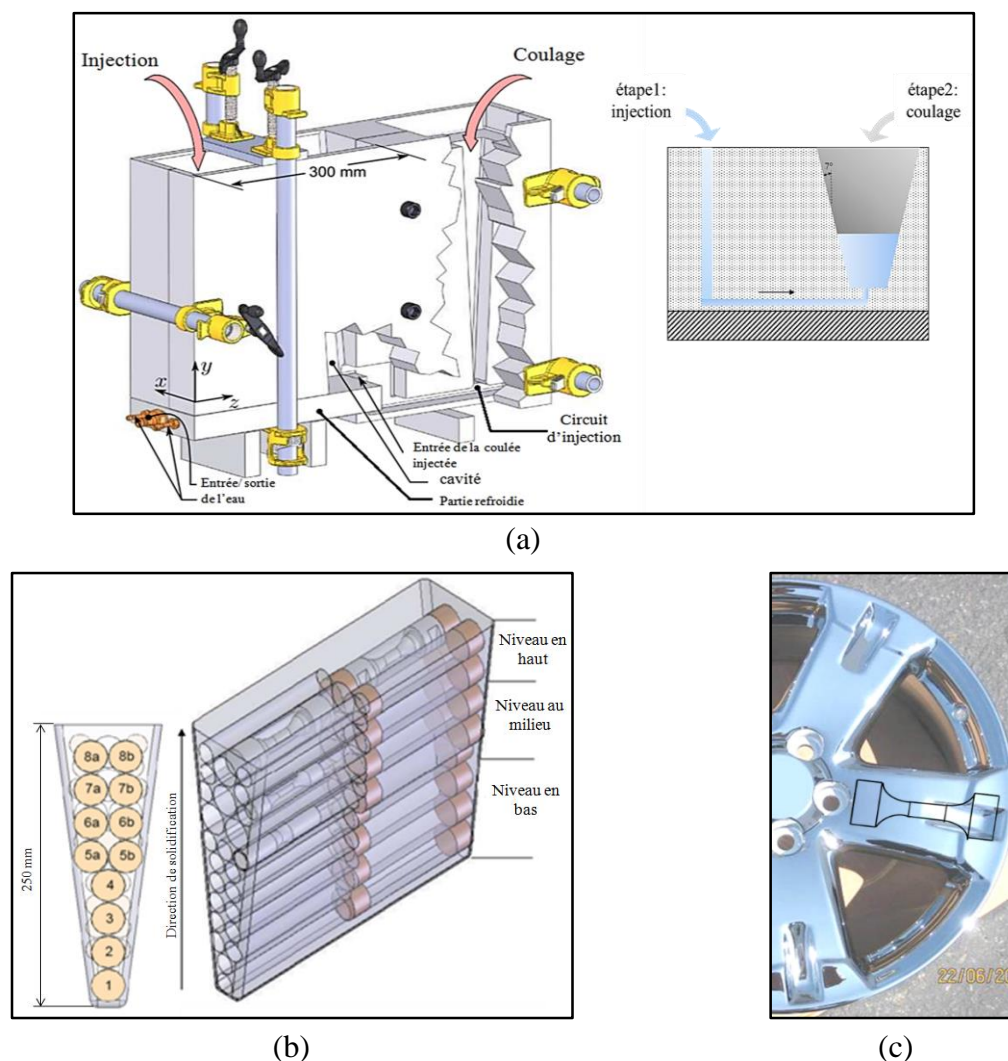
(a) Dispositif expérimental de préparation de la coulée [85] (b) géométrie de la coulée et emplacement des éprouvettes de fatigue (c) zone de prélèvement des éprouvettes issues des jantes de roue d'automobile
